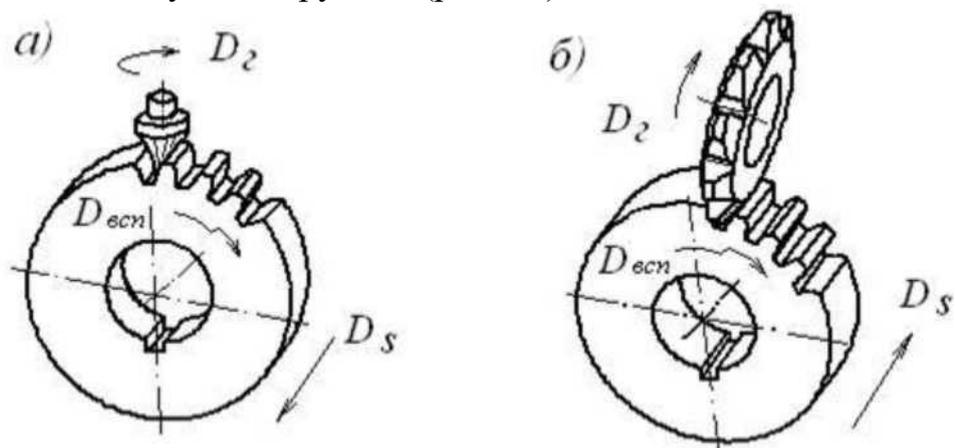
Схема фрезерування зубчастих коліс методом копіювання пальцевої (а) і дискової (б) модульної фрезою.
